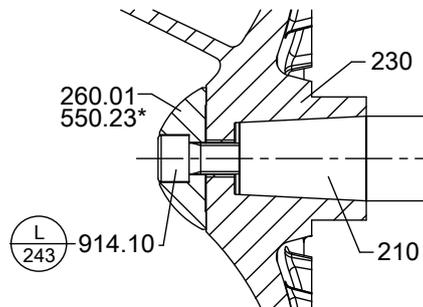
Laufradbefestigung, Baugrößen: 800-370, 800-400, 800-401
